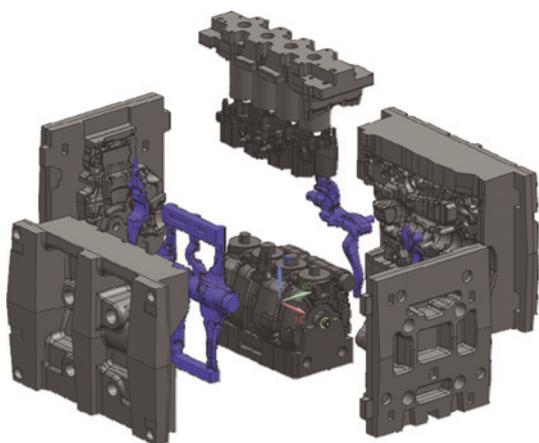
Пример стержневого пакета для получения алюминиевой отливки 4-цилиндрового рядного блока двигателя методом «пакетной формовки» (www.laempe.com) [2]
